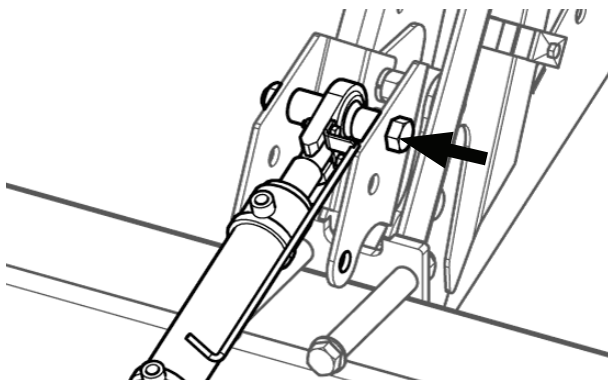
Гидравлический цилиндр наклона — верхнее монтажное отверстие
